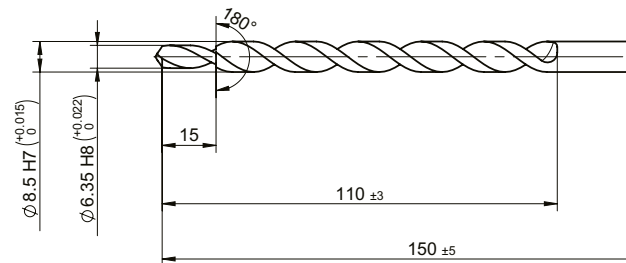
Stufenbohrer Typ 1337A2 für Montagenippel 3/8-24 UNF
